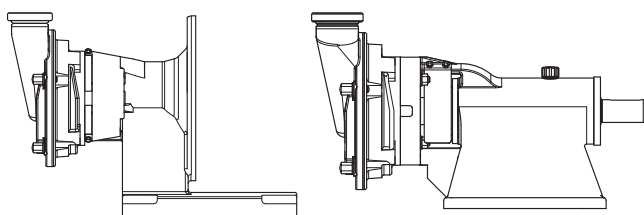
Máquina incompleta: bomba sin motor, acoplamiento y bastidor base, ejemplo basado en el tamaño constructivo KF y L
